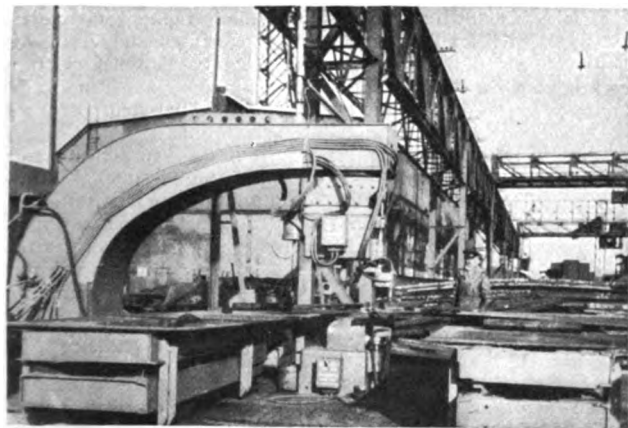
Doppelpunkt-Schweißmaschine an der Schiffshelling.
